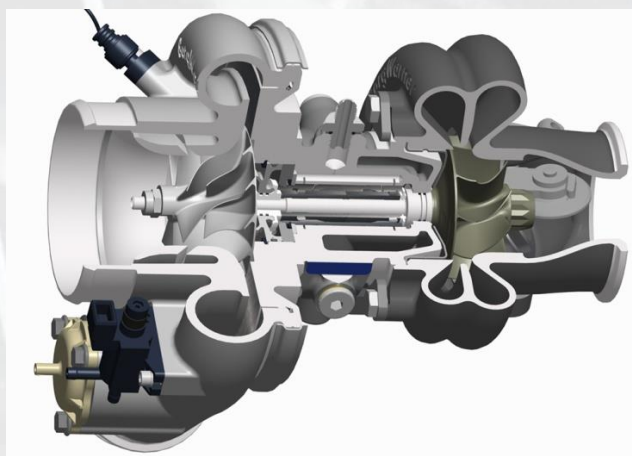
Внешний вид типичного турбокомпрессора с радиальной турбиной [8]
